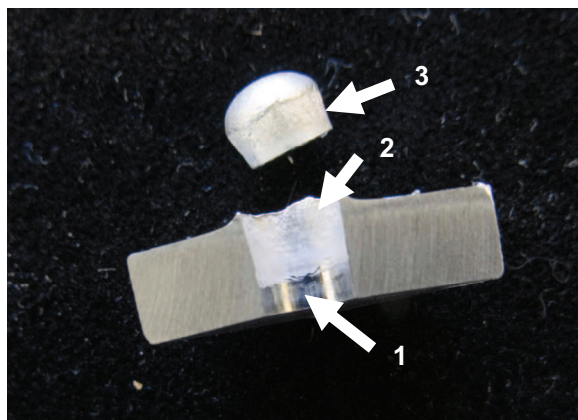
Внешний вид поверхности разрушения и пробки. Зеркальная и шероховатая поверхности разрушения на образце обозначены цифрами 1 и 2 соответственно, пробка – 3
